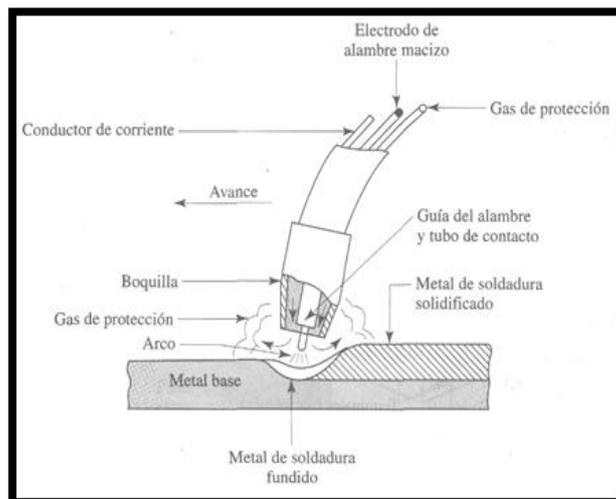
Componentes del proceso de soldadura MIG-MAG.
